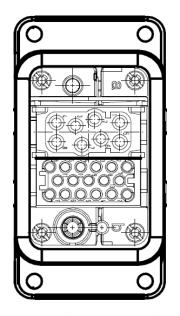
MOTOR 重载连接器: 左侧第 1、2、3 轴,右侧第 4 轴
